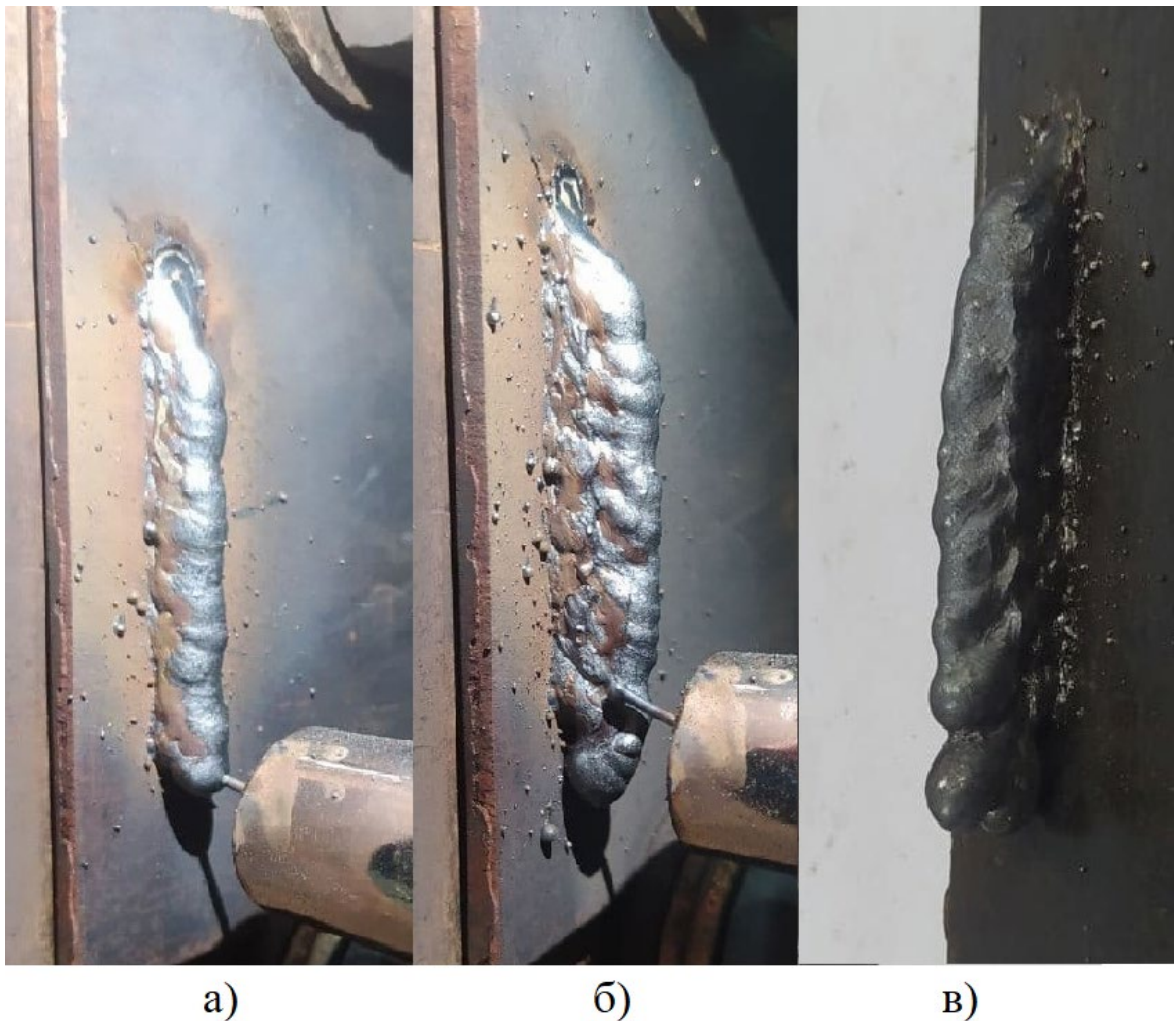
Наплавлення стінки довжиною 60 мм., а) один наплавлений шар; б) два наплавлених шари; в) три наплавлених шари
